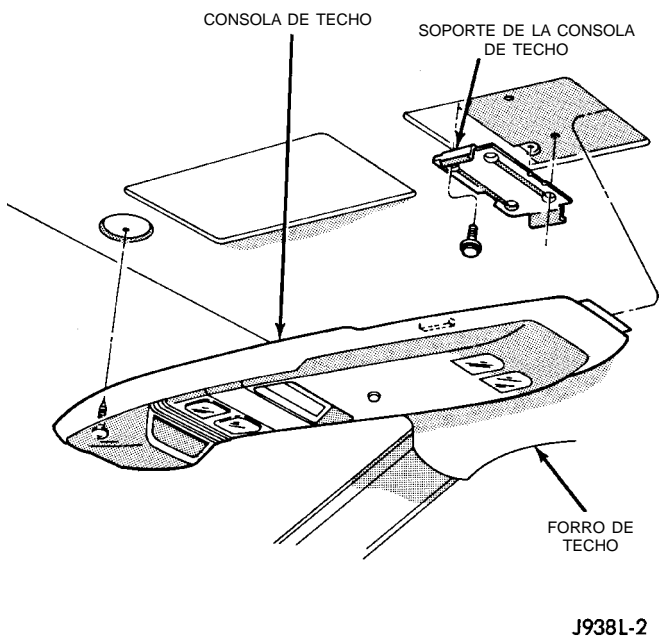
Desmontaje/instalación de la consola de techo - versión larga
